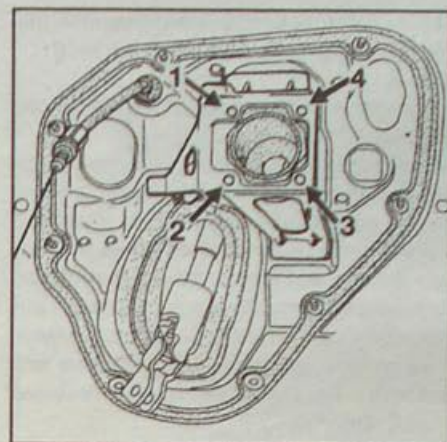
Расположение гаек крепления вакуумного усилителя тормозов
